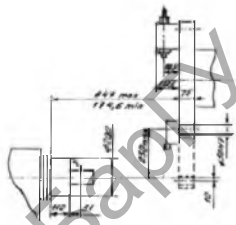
Рабочее пространство станка 1П420ПФ40
